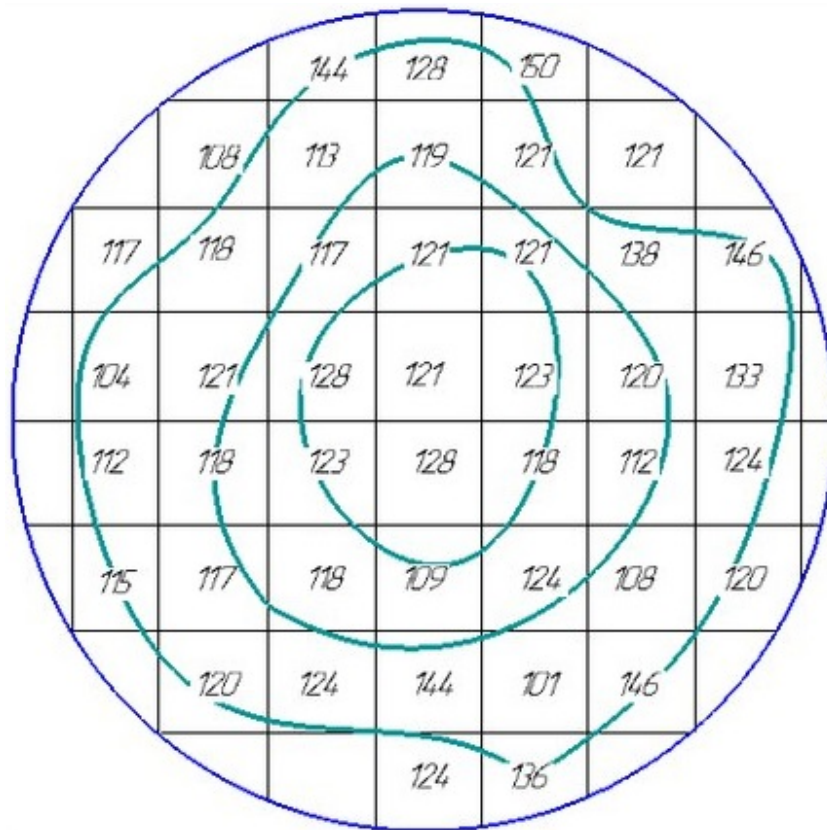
Линии изосклер на поверхности торца осаженной заготовки
